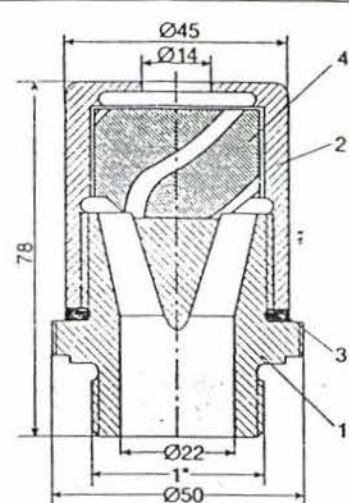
Duza de pulverizare Ø 14 mm:
